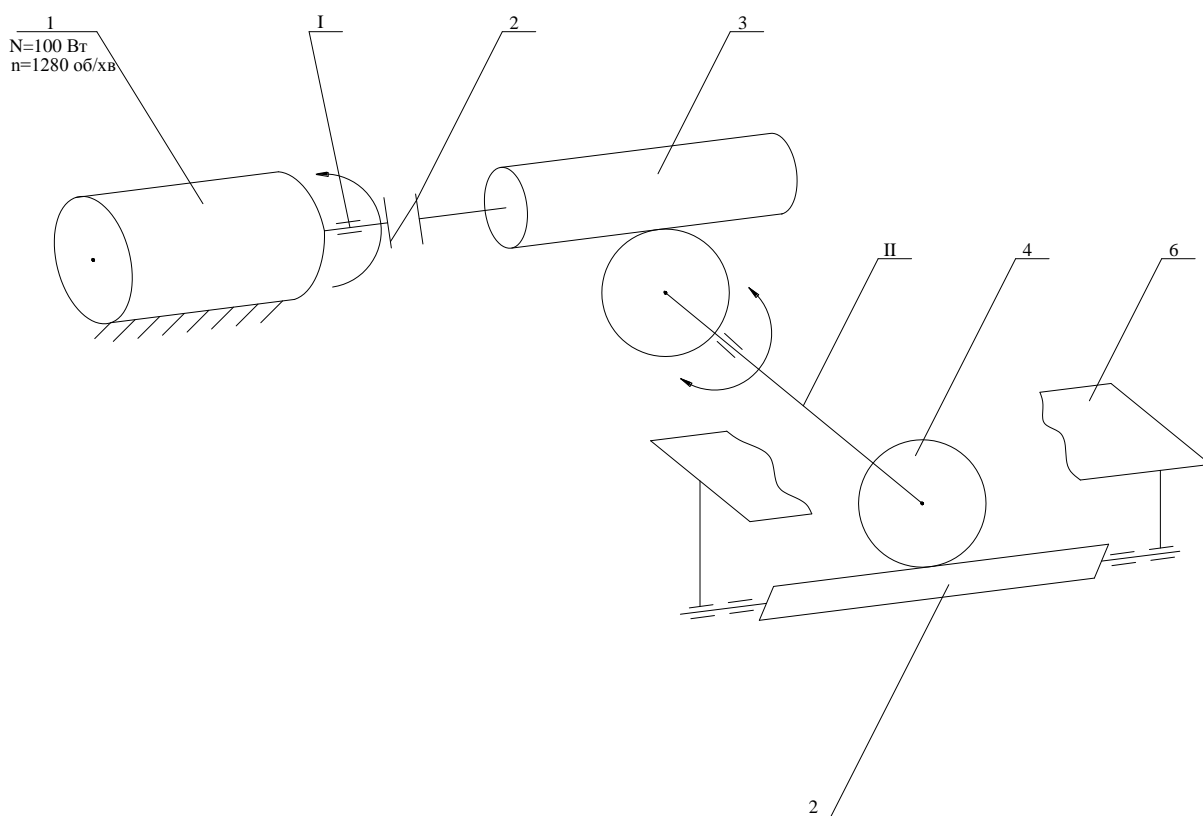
Кінематична схема пристрою для зварювання
